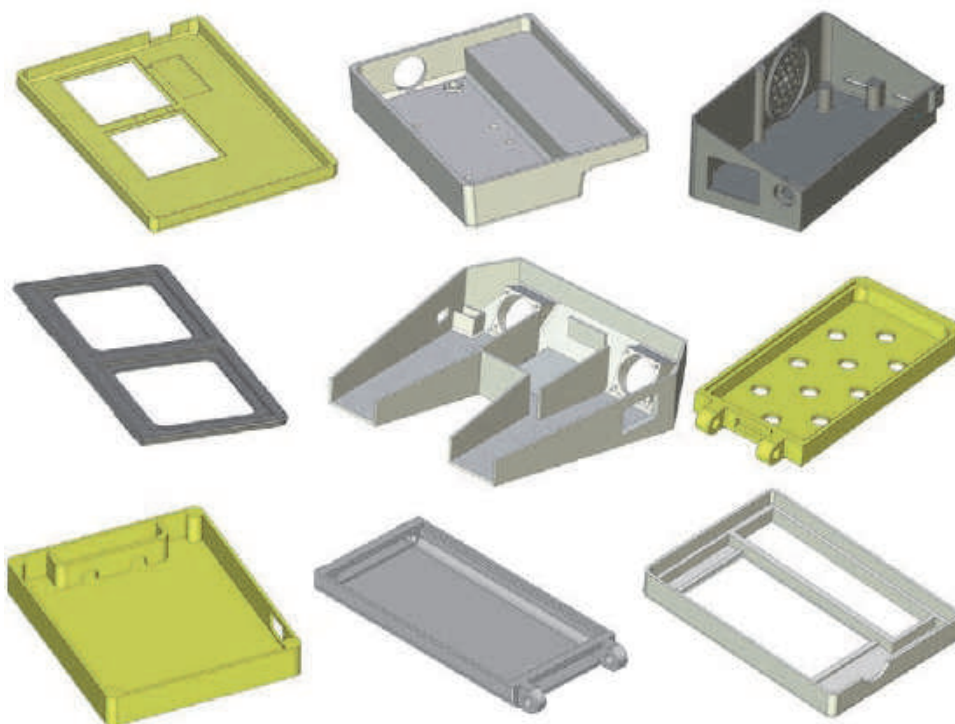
Корпусные детали электронных устройств с солнечными батареями, изготовленные на FDM-принтере
